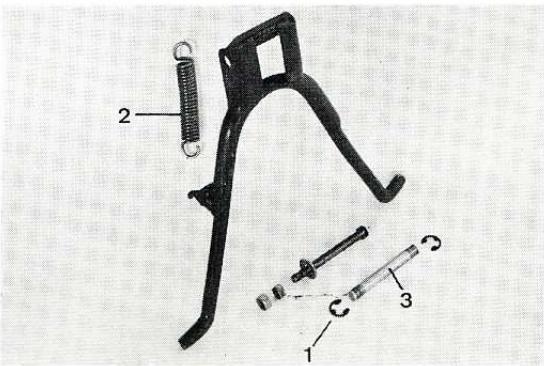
DEMONTAGE DE LA BEQUILLE.
